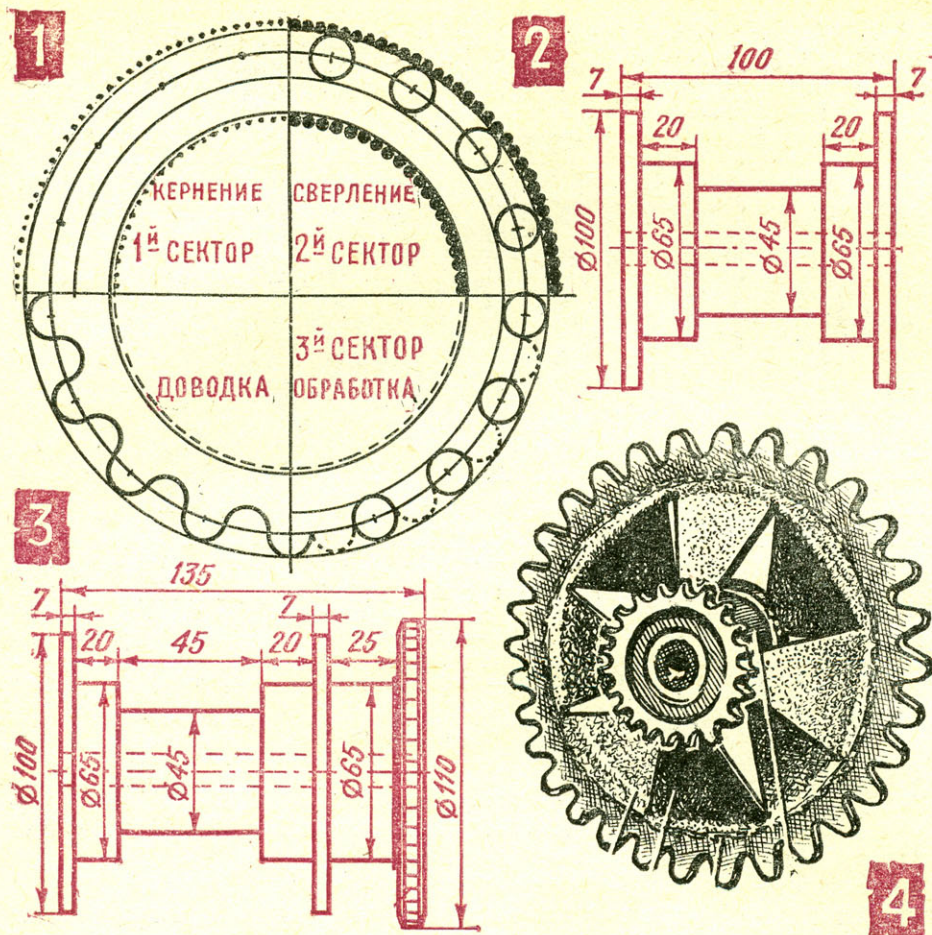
Конструкция зубчатых колес гусеничной ленты:
